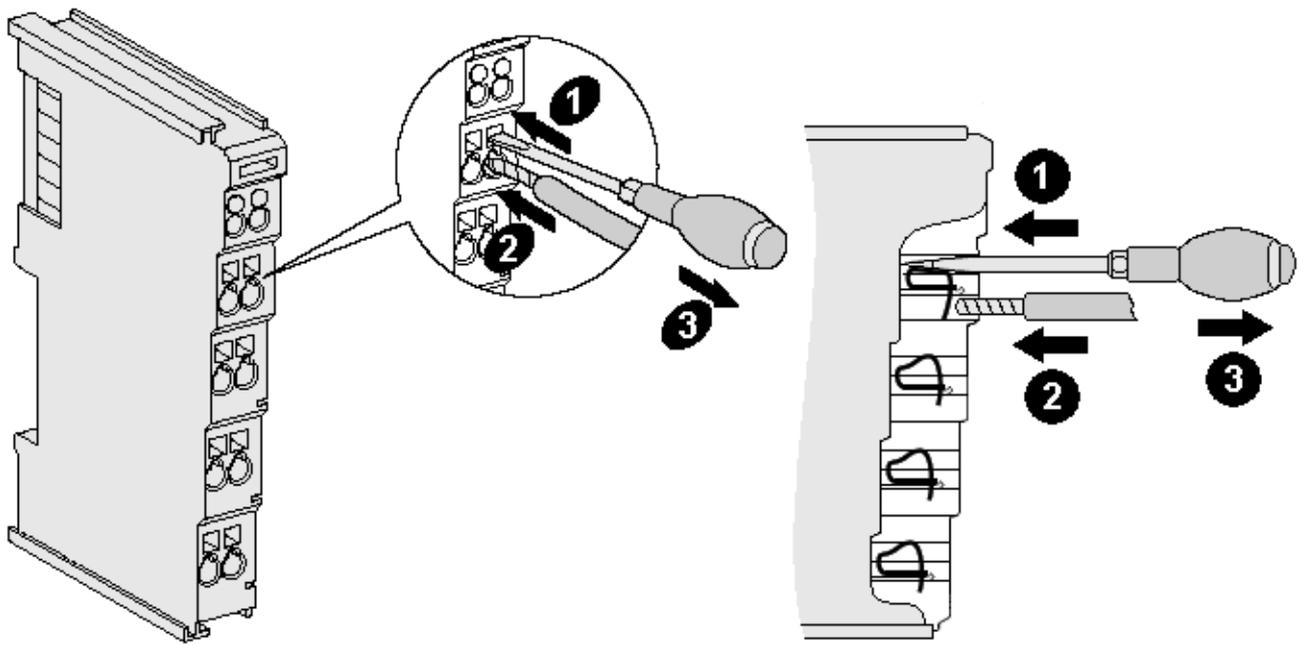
Anschluss einer Leitung an eine Klemmstelle
